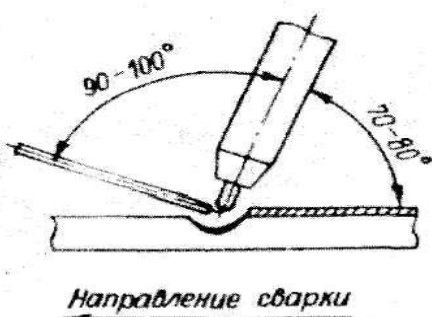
Схема ручной сварки титана неплавящимся электродом
